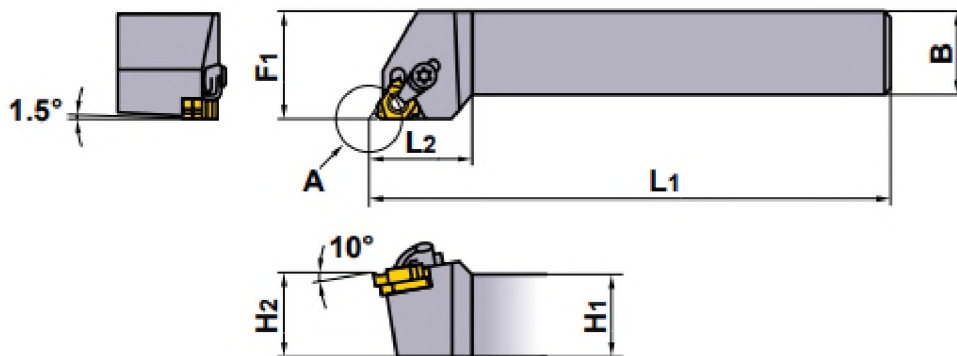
Державка MMTER1212H16-C [3 с. 445]
